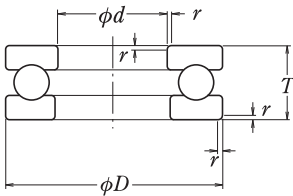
Rodamientos de Bolas de Empuje de Una Sola Dirección
